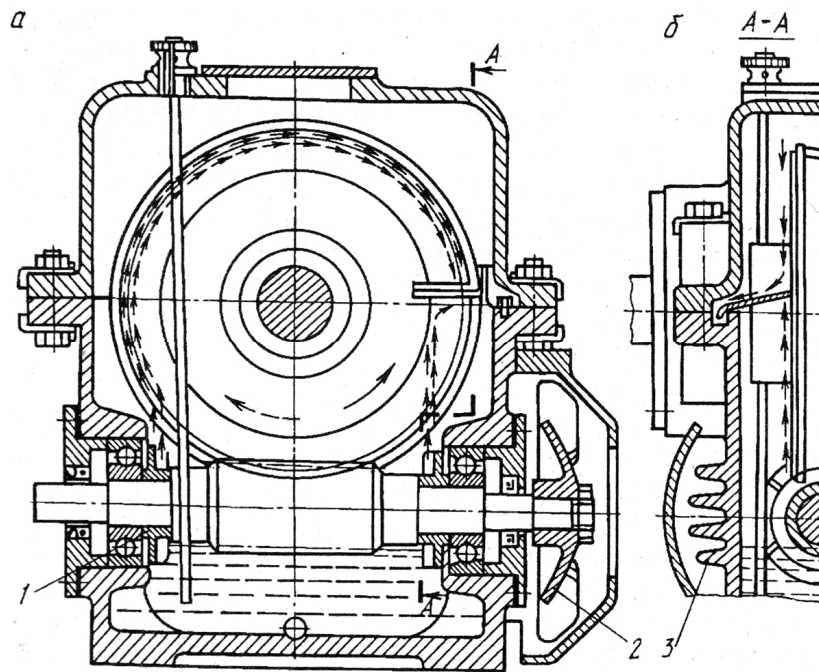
Червячный редуктор с воздушным охлаждением: *а* – разрез по валу червячного колеса; *б* – разрез по валу червяка; 1 – брызговик; 2 – крыльчатка; 3 – ребра
